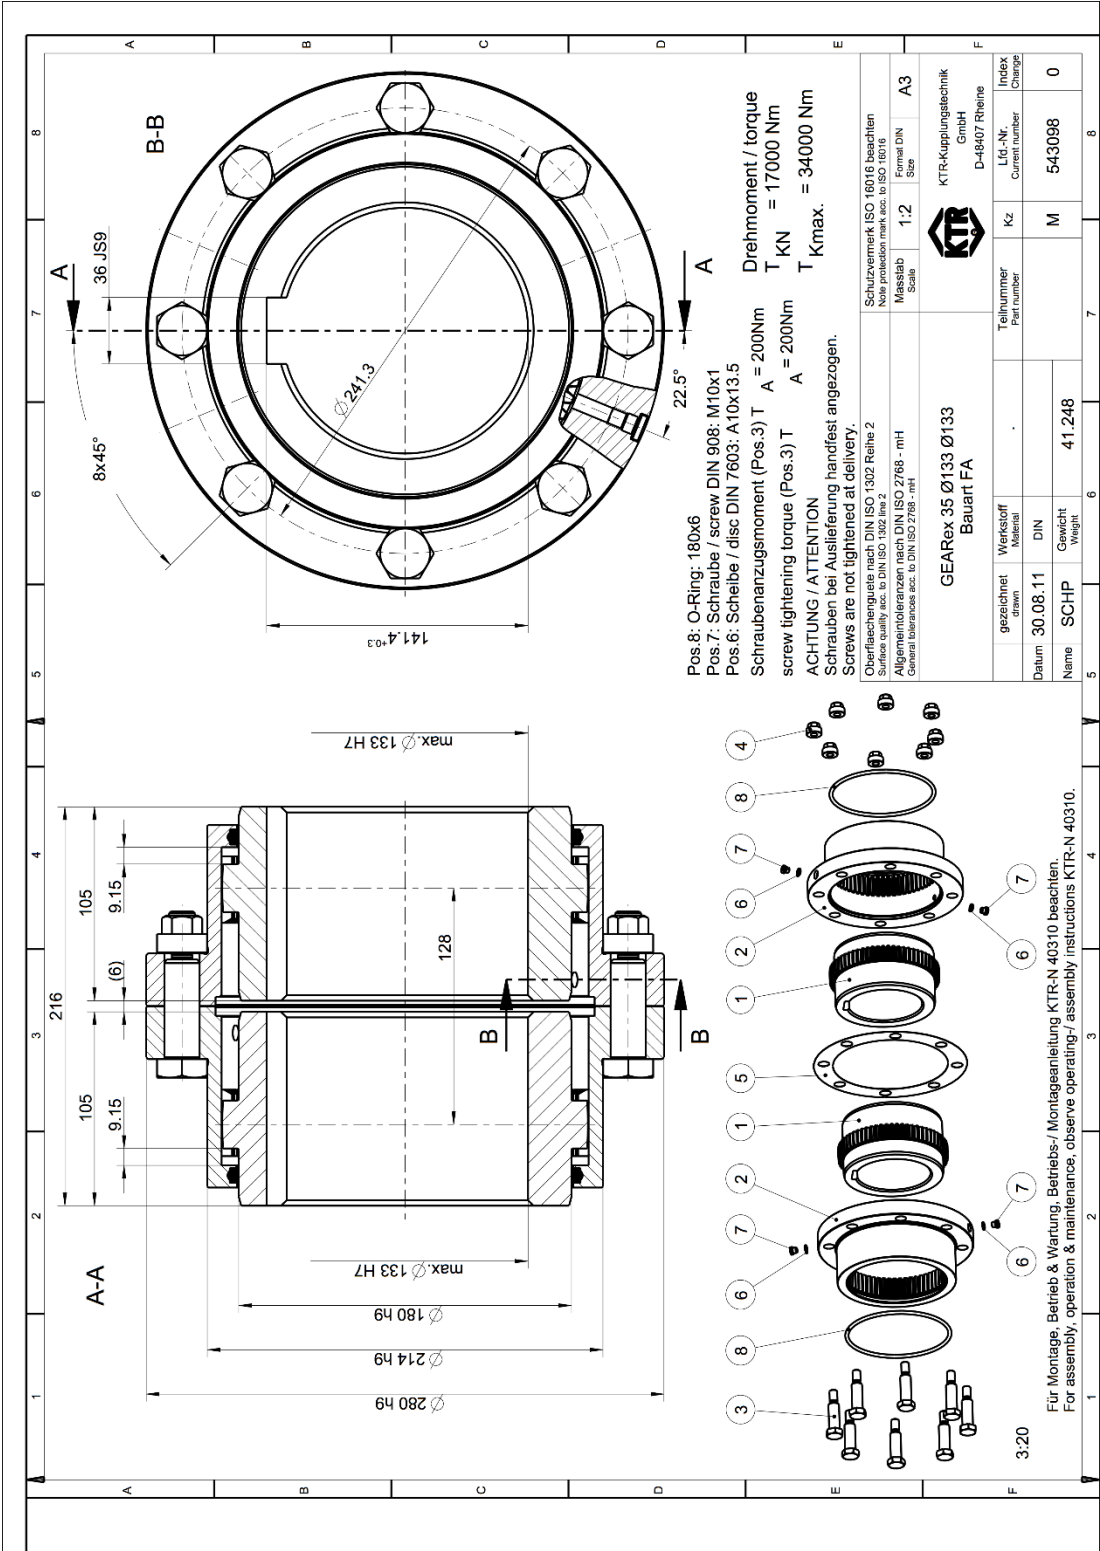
Desenhos técnicos do acoplamento GearEx FA 35.
